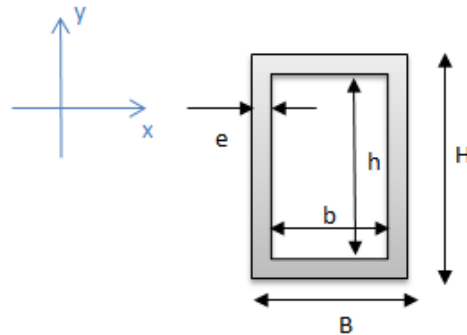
Dimensiones de las Vigas del Soporte Principal
